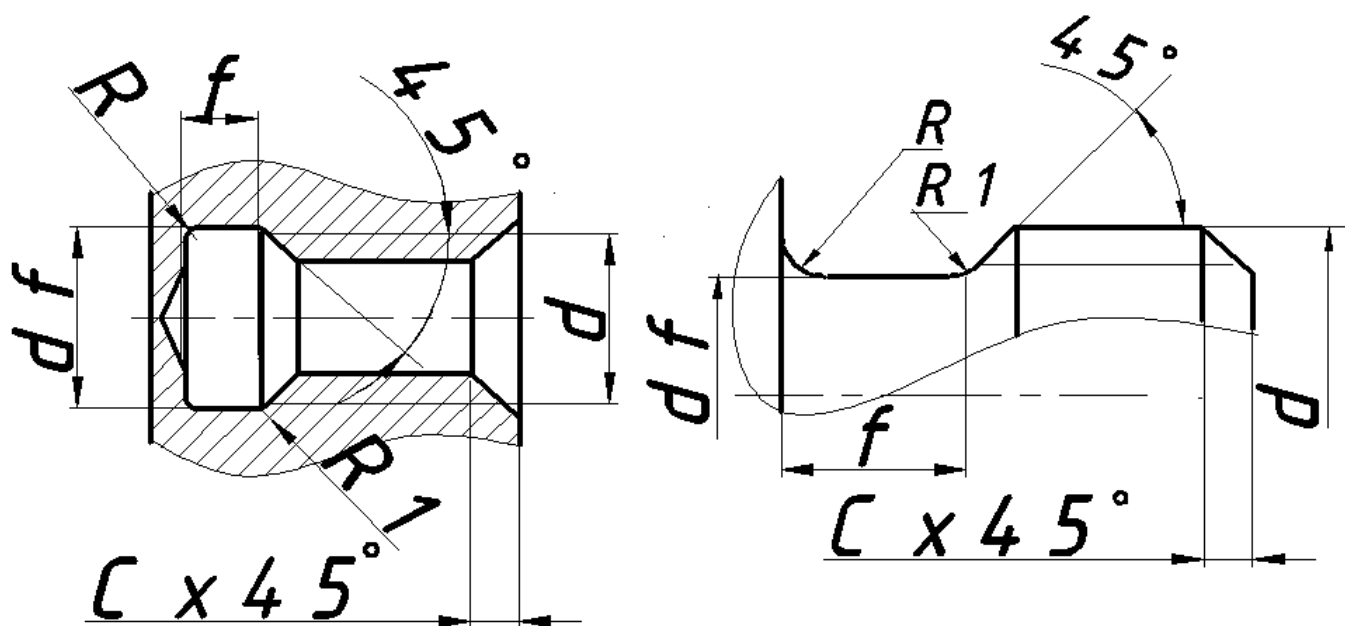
Проточки и фаски трубной цилиндрической резьбы
